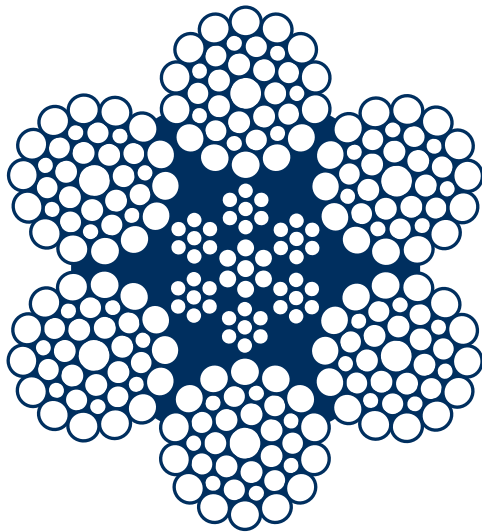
Drahtseil 6x36 Warrington-Seale mit Stahleinlage
